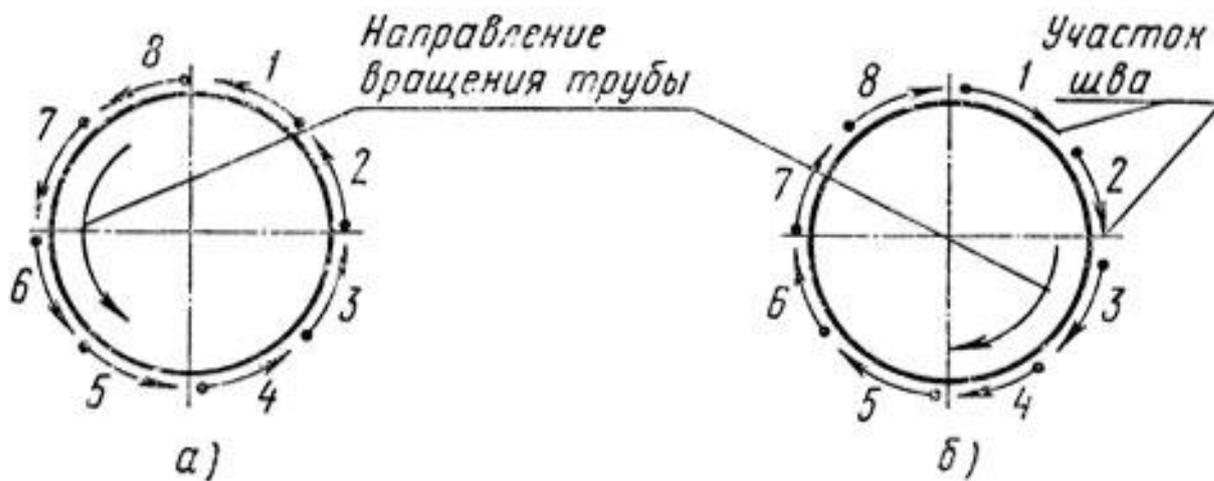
Схема сварки стыка труб большого диаметра: а - первого слоя, б - второго слоя
